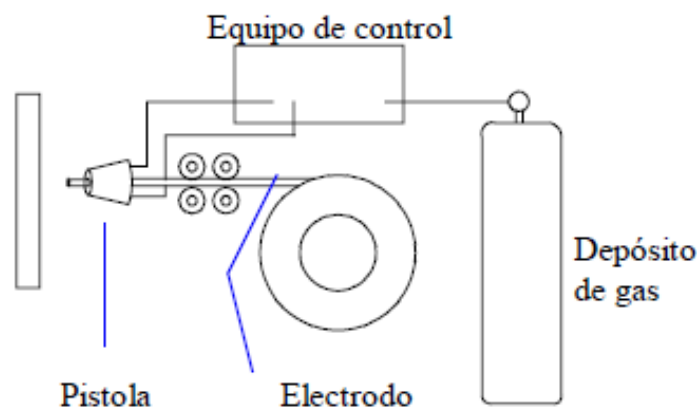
Representación de sistema de soldadura MIG [9].
